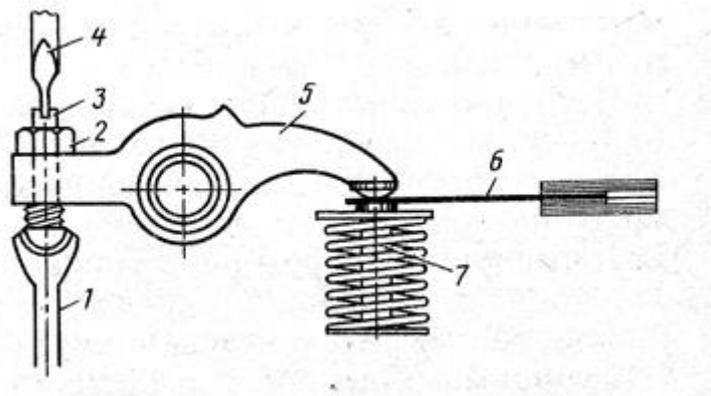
Регулировка зазоров в газораспределительном механизме:
